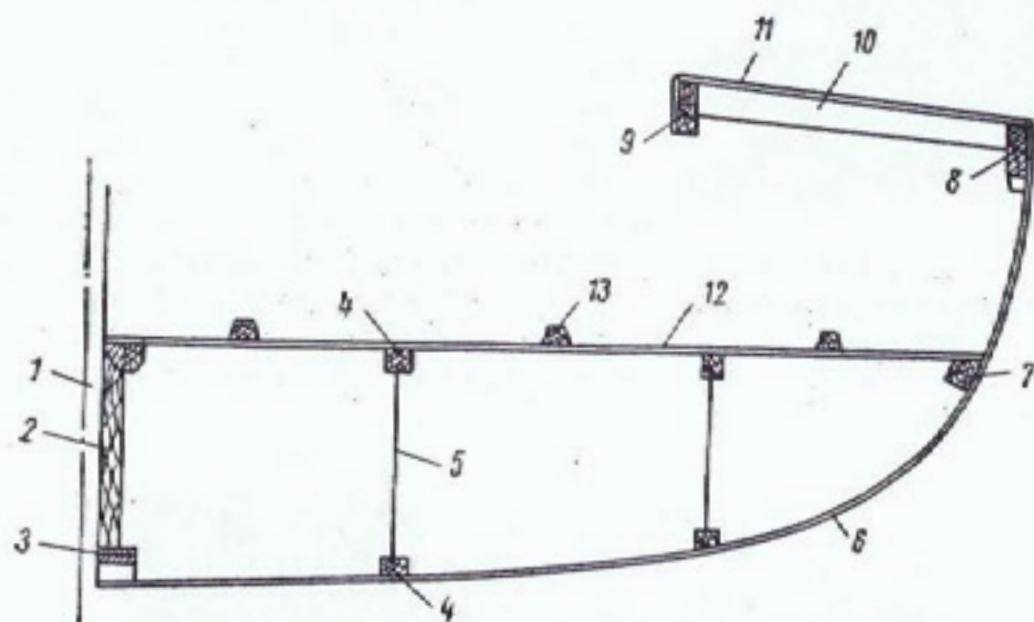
Схематический поперечный разрез швертбота скорлупной конструкции с двойным дном
